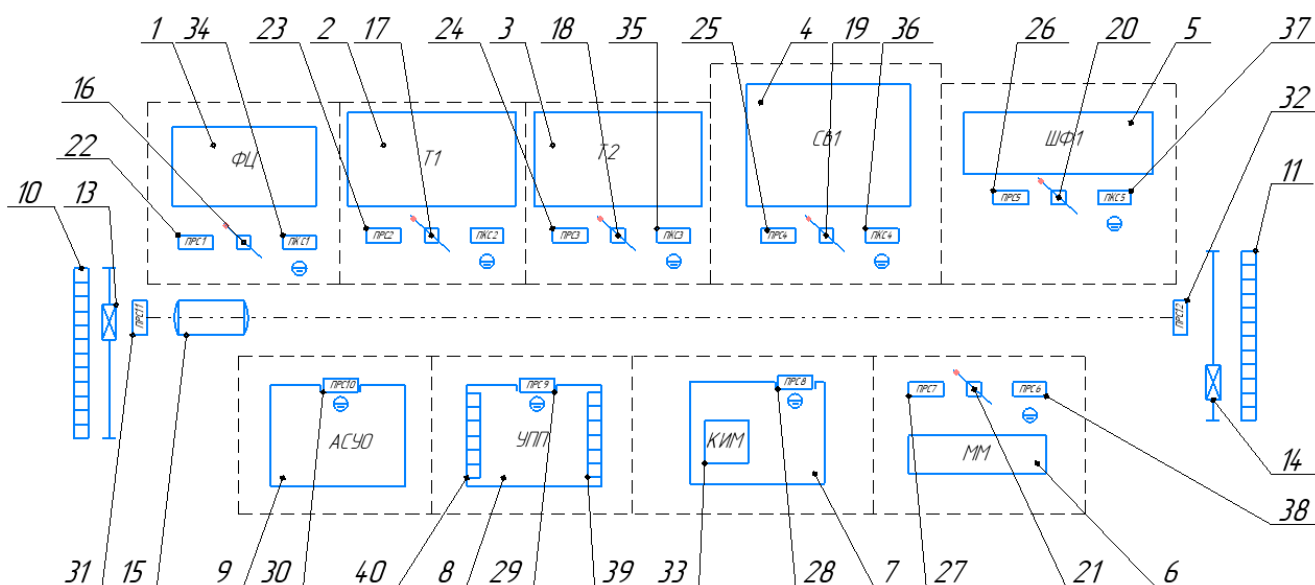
Структурная схема ГПС: 1 – фрезерно-центровальный станок МР-73М; 2 – токарный станок СТХ esoline; 3 - токарный станок СТХ esoline; 4 – вертикально-фрезерный станок DMC 650 V; 5 – шлицефрезерный станок 5350А; 6 – моечная машина; 7 – участок контроля; 8 – участок подготовки производства; 9 – автоматизированная система уборки отходов; 10 – склад заготовок; 11 – склад готовой продукции; 13, 14 – кран-штабелер; 15 – робокар; 16 – 21 – промышленный робот; 22 – 32, 38 – приемно-раздаточный стол; 33 – контрольно-измерительная машина; 34 – 37 – промежуточный контрольный стол; 39 – склад режущих инструментов; 40 – склад заготовок.
